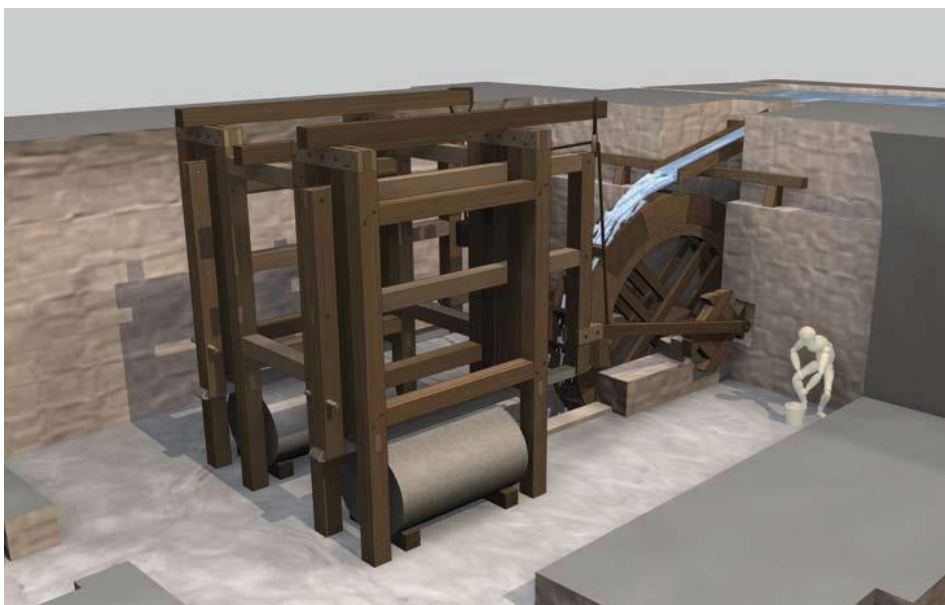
Disseny de la màquina de serrar de Thierry Morin i Jacques Seigne.
